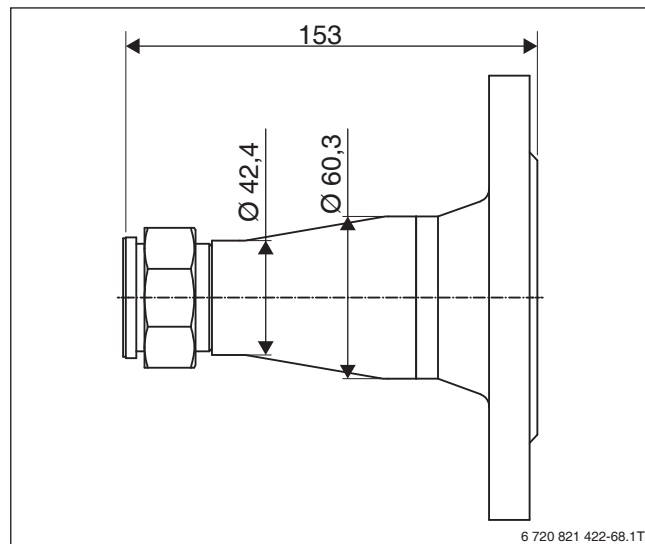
Übergangsstück DN 50/PN 16 – G 1 ½ " (Maße in mm)
